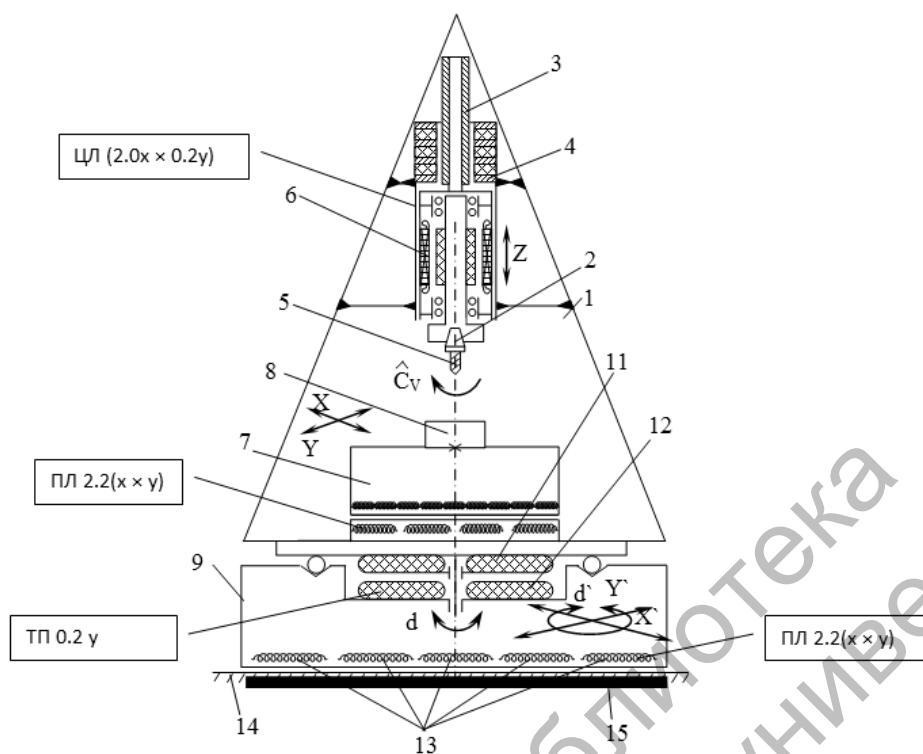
Многокоординатный мобильный сверлильно-фрезерный станок будущего без механических передач по патенту на изобретение № 101447 с генетическими формулами узлов (механизмов)
